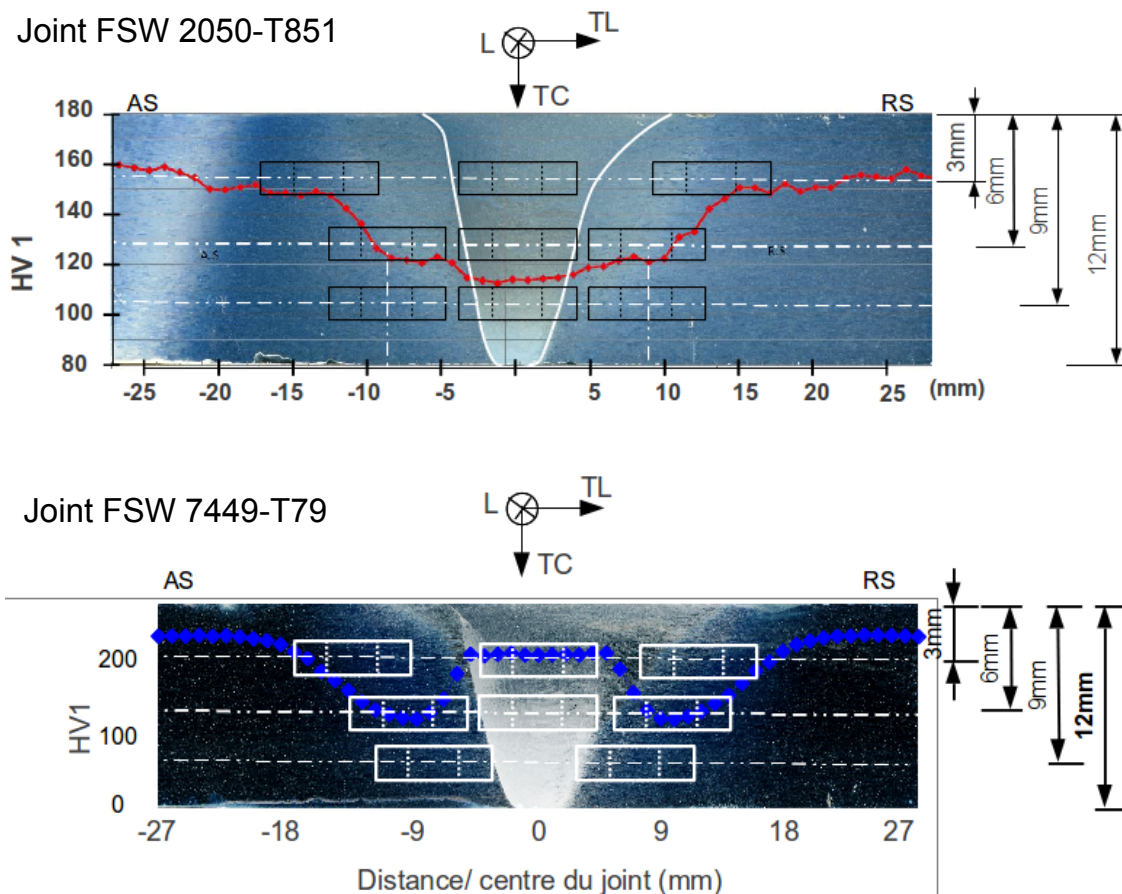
Schéma de prélèvement des mini-éprouvettes dans l'épaisseur des joints soudés par FSW
